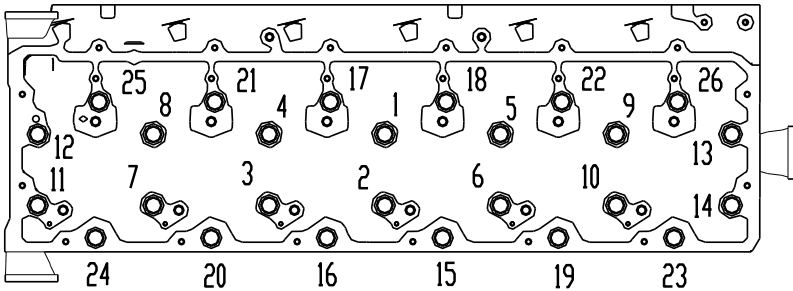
Порядок затяжки болтов крепления головки цилиндров
